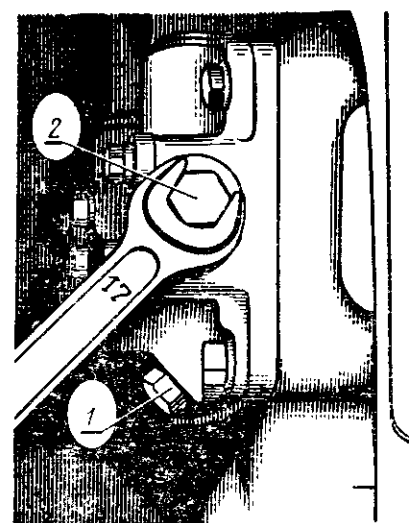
Пробки контрольных отверстий для проверки уровня масла в коробке передач:
